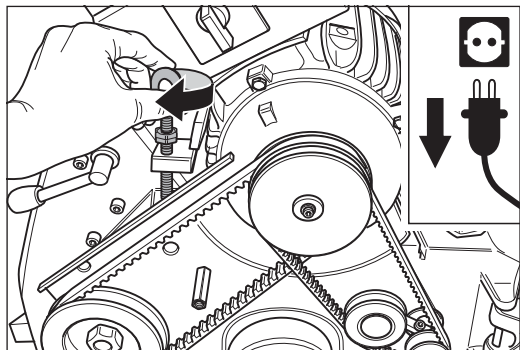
Die beiden Keilriemen auflegen und mit der Spannschraube am Motor spannen.
